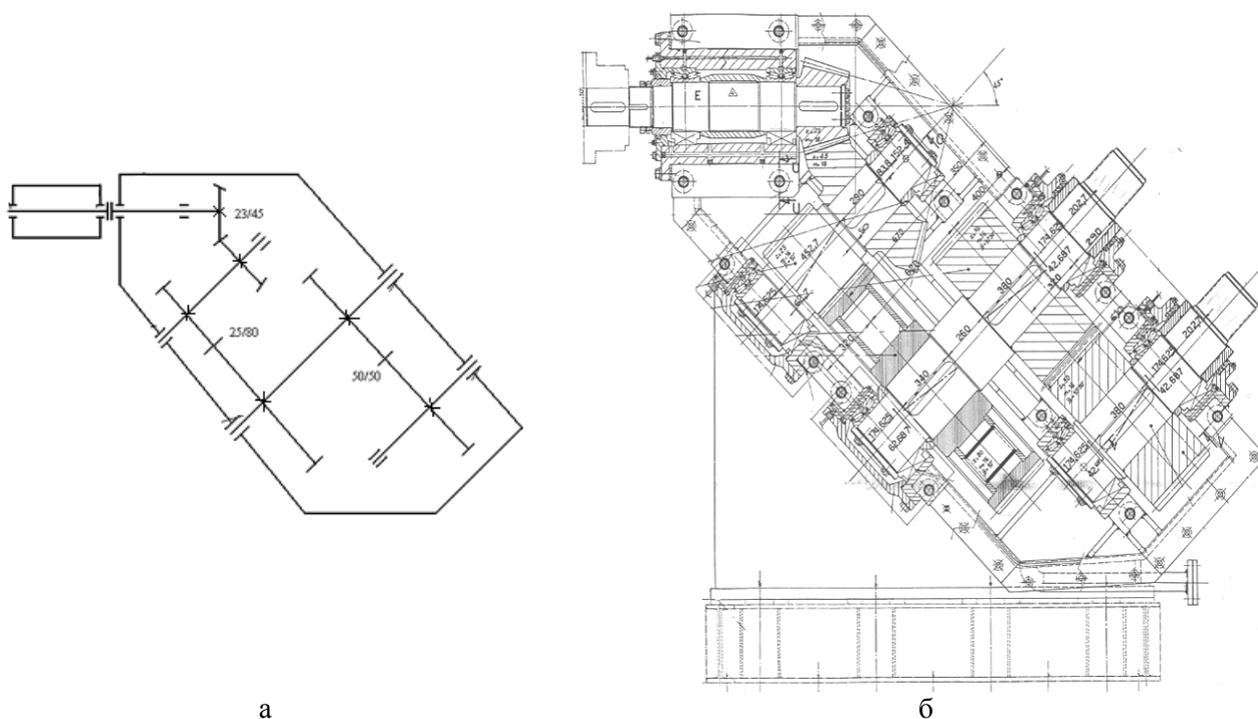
Кинематическая схема (а) и чертеж в разрезе (б) редуктора привода прокатных клетей калибровочного стана
